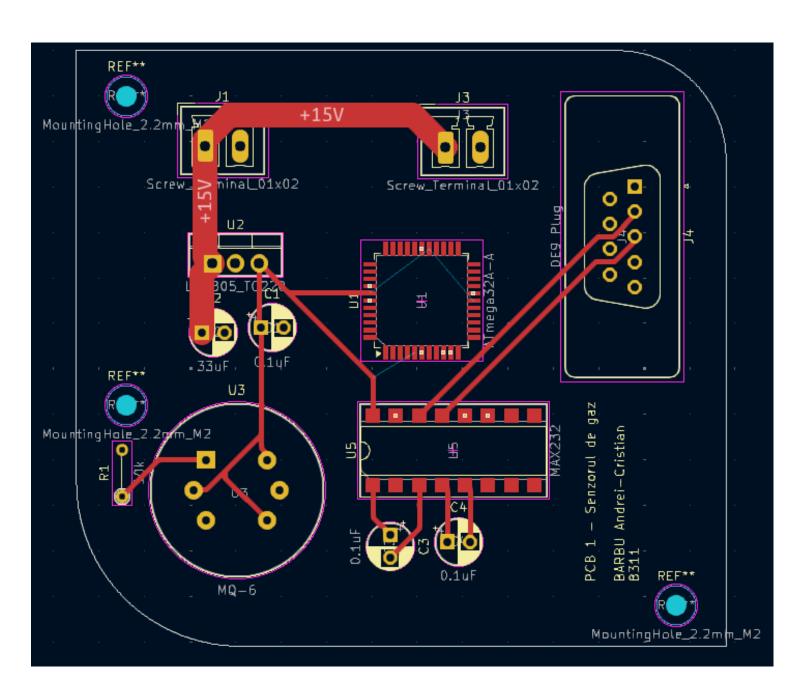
Cablaj imprimat din KiCad (Front Layer)
